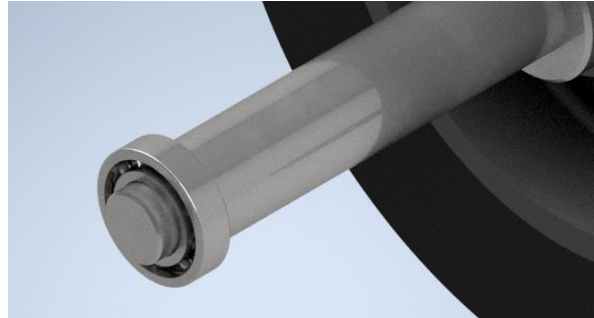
Primer rodamiento insertado en el eje de impulsión
